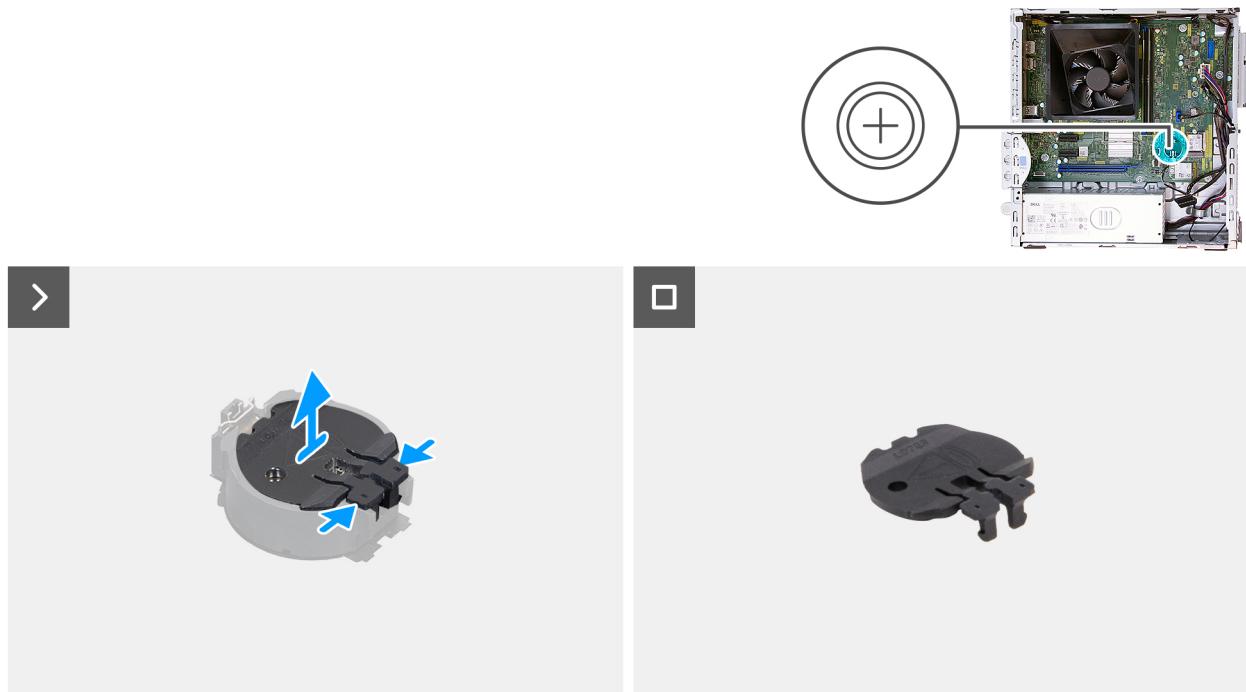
Extracción de la cubierta de la batería de tipo botón
